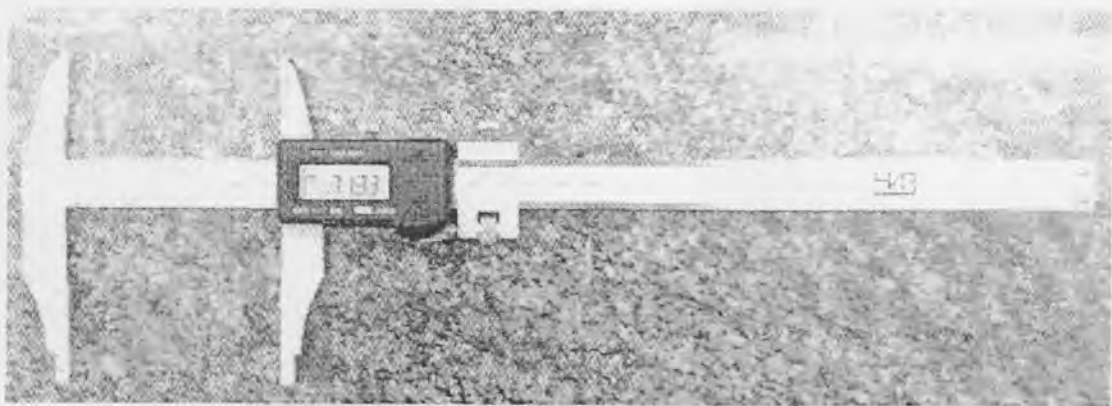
Штангенциркуль ШЦЦ-II.
